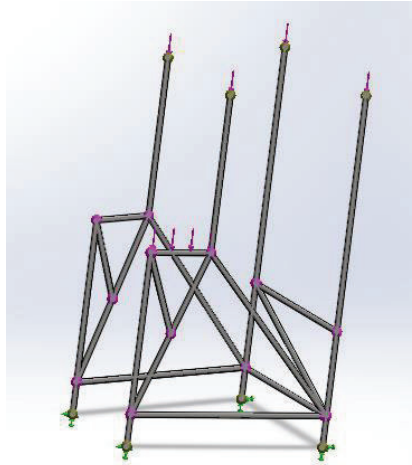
43 Restricciones y Cargas externas sobre la estructura
